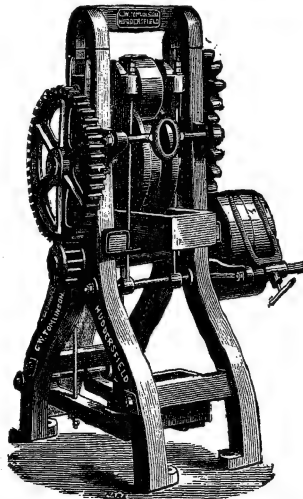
Quetschmaschine für Wollengewebe im Strang.
